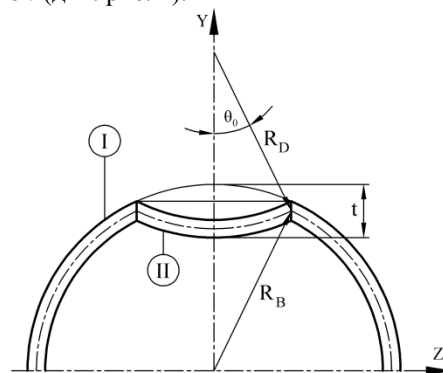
Поперечний переріз ділянки циліндричної обичайки з вм'ятиною
